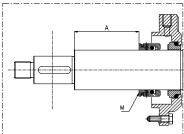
Установочный размер А, диаметр вала 28 мм и 43 мм
